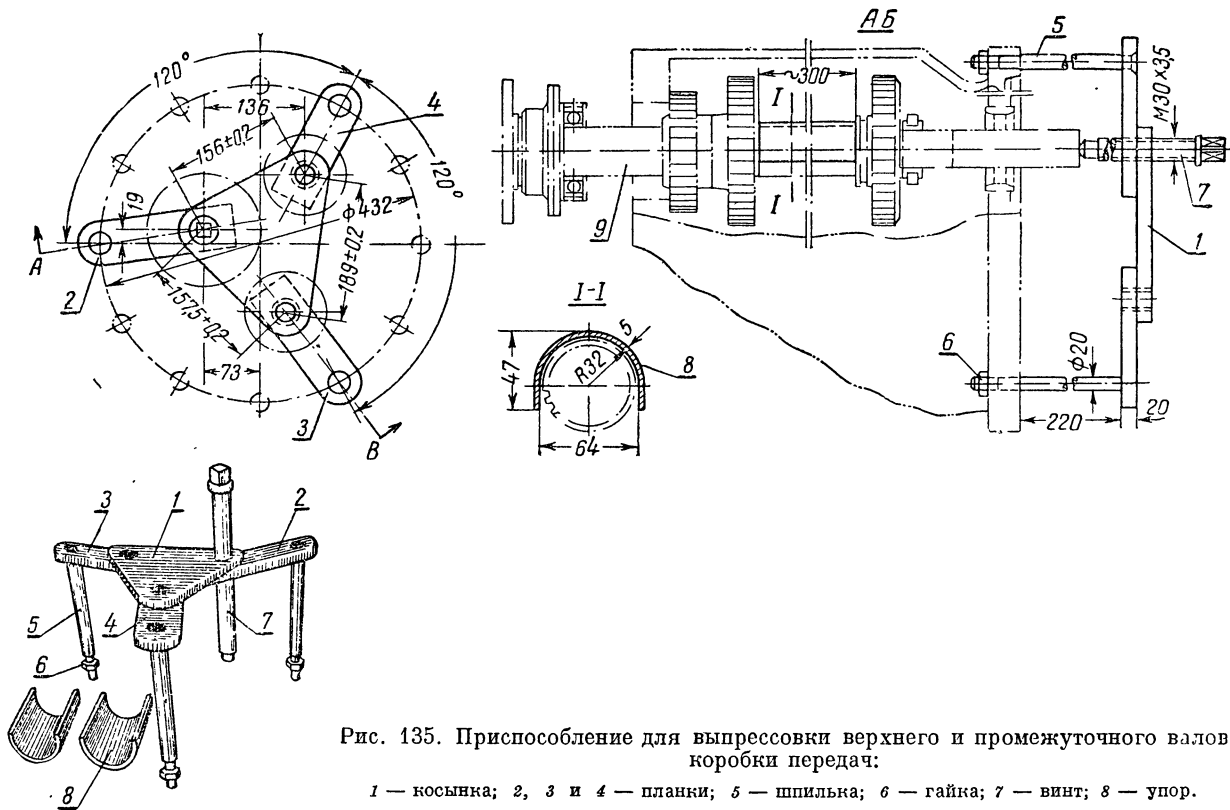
Приспособление для выпрессовки верхнего и промежуточного валов коробки передач:
